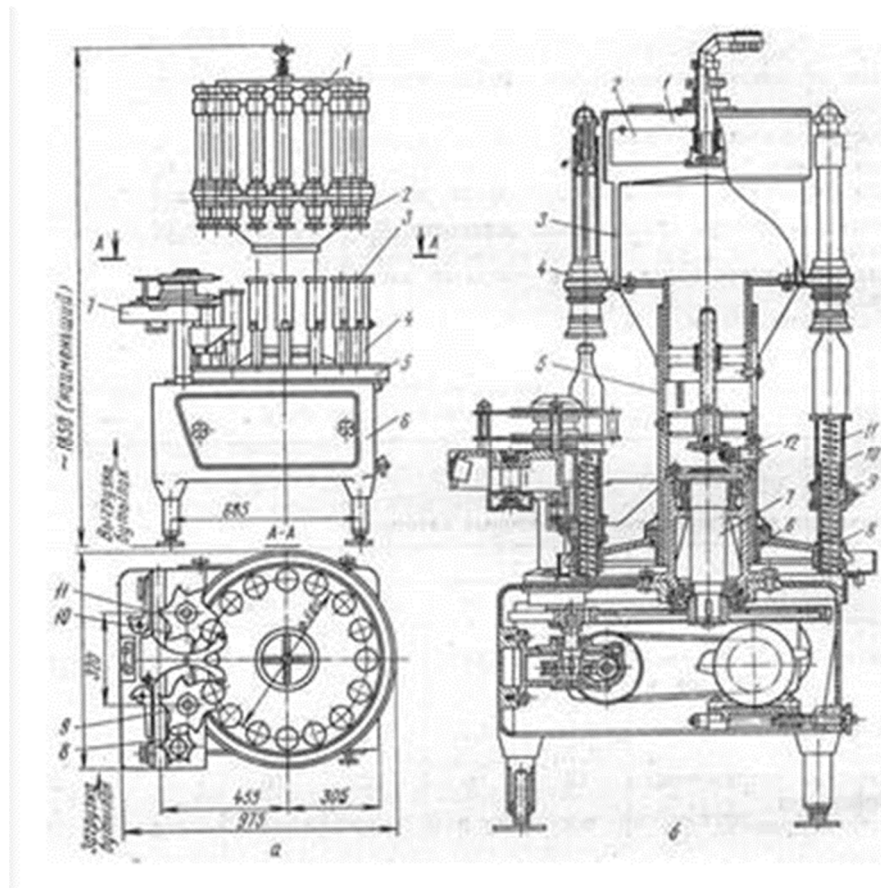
Машина для фасування ВАР-6: *а* - загальний вигляд; *б* - розріз: 1 - резервуар; 2 - поплавков; 3 - колектор; 4 - дозатор; 5 - стійка; 6 - карусель; 7 - вал; 8 - підйомний столик; 9 - ролик; 10 - пружина; 11 - відсікач; 12 - завантажувальна зірочка; 13 - розвантажувальна зірочка; 14 - електродвигун
